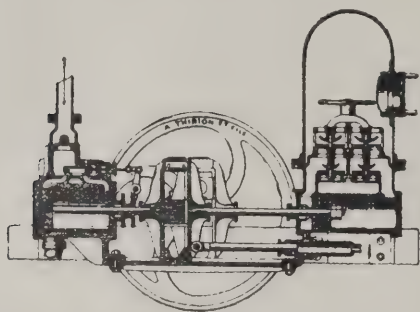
Coupe de la première pompe à vapeur à incendie.
